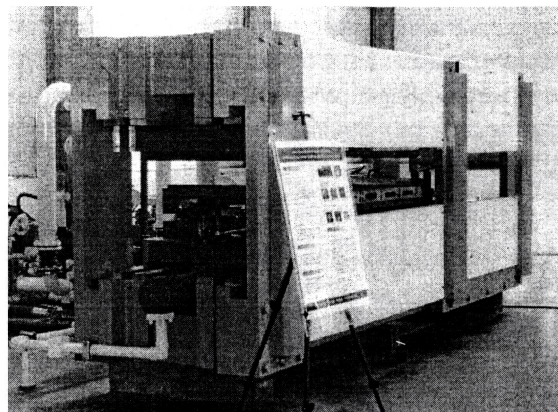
Стан ПМ 5.155 конструкции ФТИ НАН Беларуси
